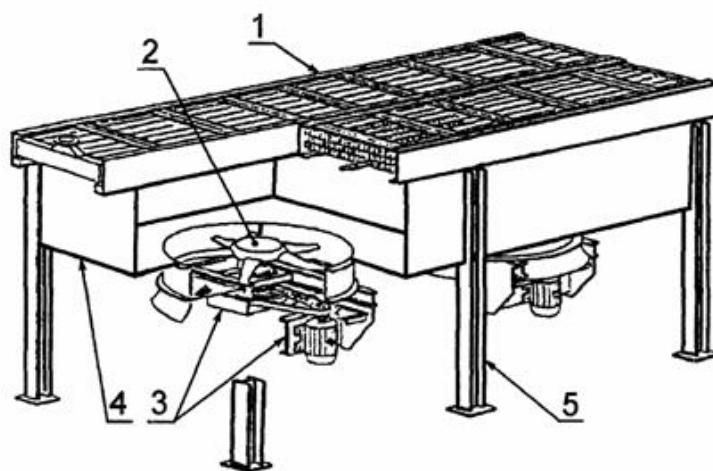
АВО нагнетательного вида: 1 – теплообменная секция; 2 – колесо вентилятора; 3 – привод вентилятора; 4 – диффузор с коллектором; 5 – металлоконструкция
